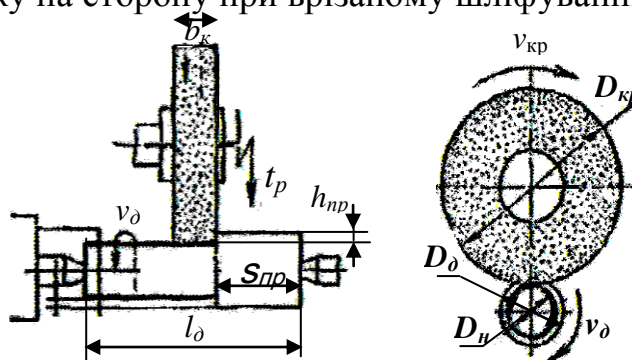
Схема обробки шліфувальним кругом деталей класу "вали":
